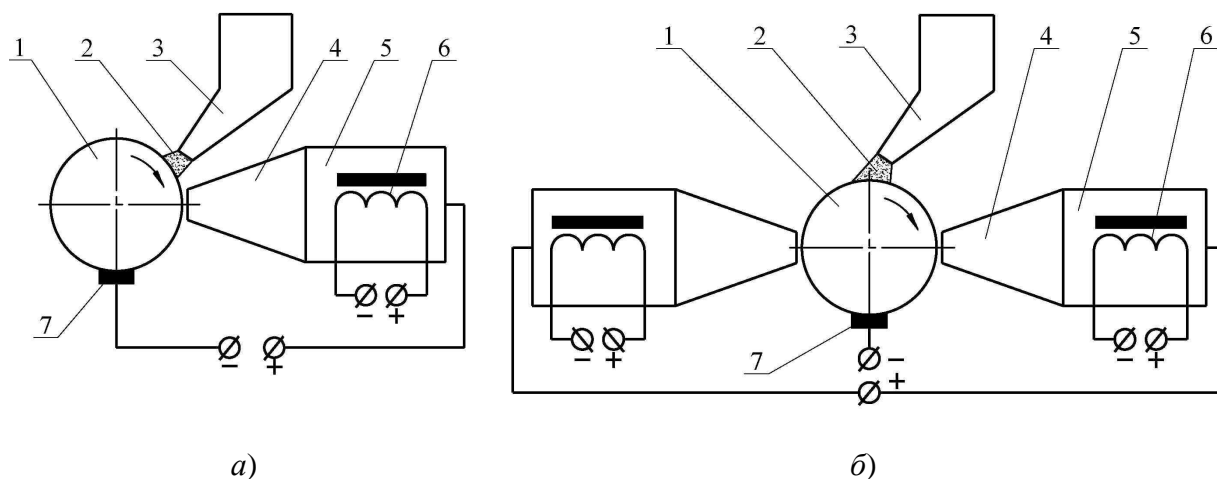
Схема установки для электромагнитной наплавки: *а* – однополюсной; *б* – двухполюсной; 1 – заготовка, 2 – порошок, 3 – бункер, 4 – наконечник, 5 – корпус, 6 – электромагнит, 7 – щетка
